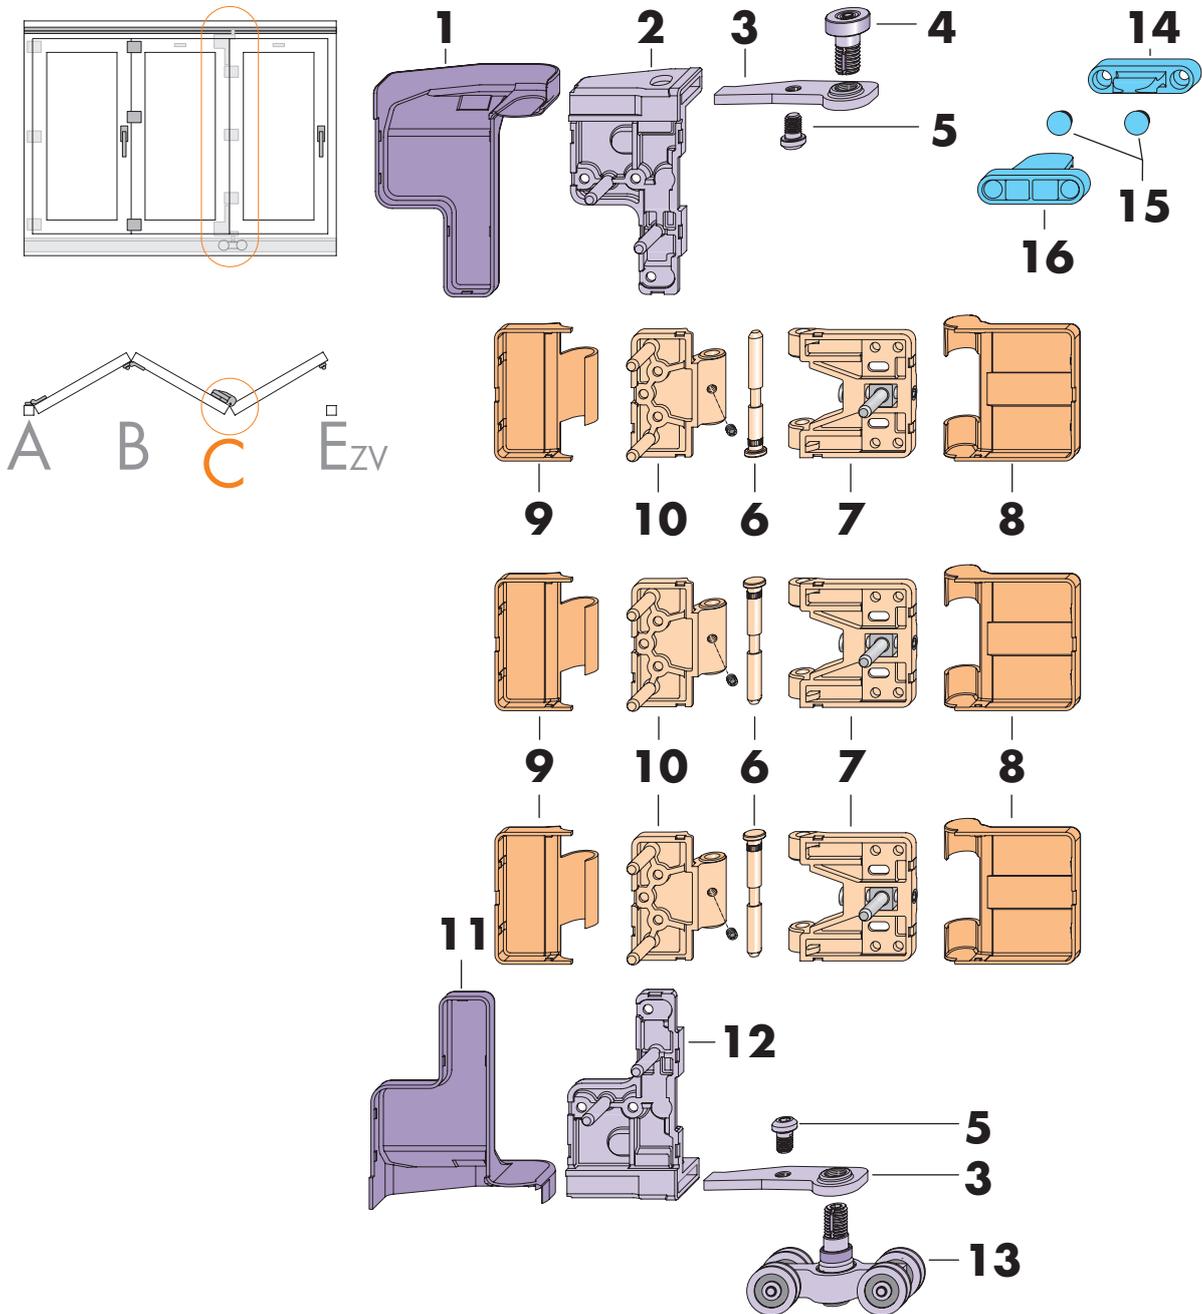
Beschlagabbildung Schnittpunkt C Bänder-FS 27/48 - Holz-/ Kunststoff Elemente außenlaufend
